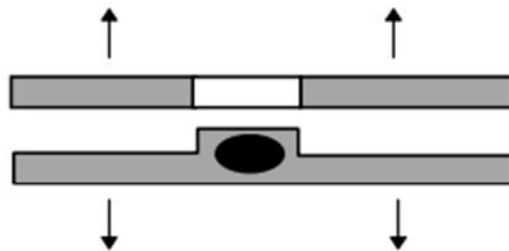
Déboutonnage d'un point soudé.
